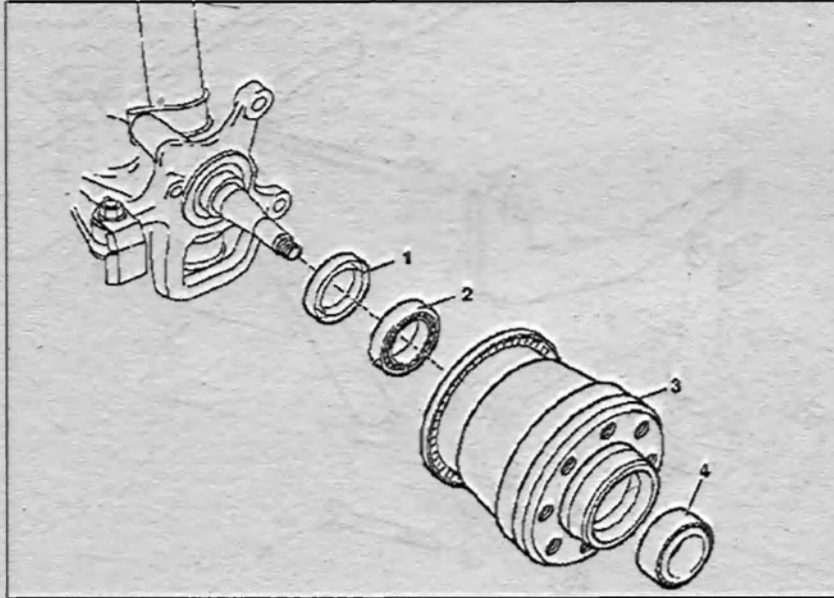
Разборка и сборка ступицы переднего колеса:
